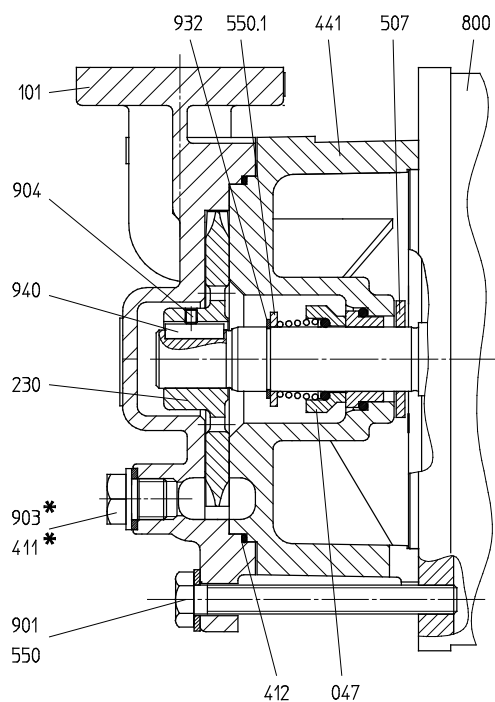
Schnittzeichnung Y-6091 (Messing)
